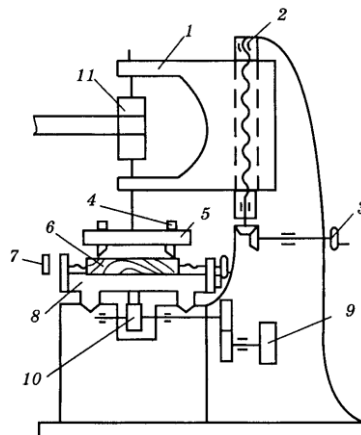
Стругальний верстат конструкції Муїра (1827 р.): 1 – супорт; 2 – напрямні супорта; 3 – ручка піднімання та опускання супорта; 4 – різці; 5 – ножовий диск; 6 – заготівка; 7 – гвинт затискання заготівки на платформі; 8 – рухома платформа; 9 – шків механізму подачі; 10 – ланцюгова передача; 11 – шків на валу ножового диска
